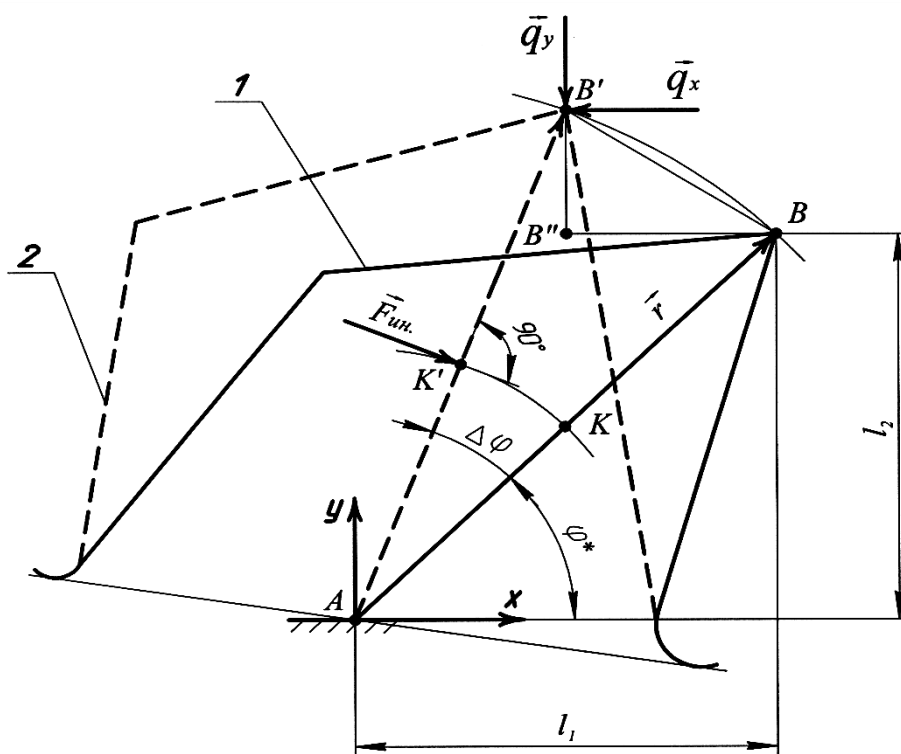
Расчетная схема нагружения вершины режущего зуба прошивки силами, возникающими в процессе резания:
